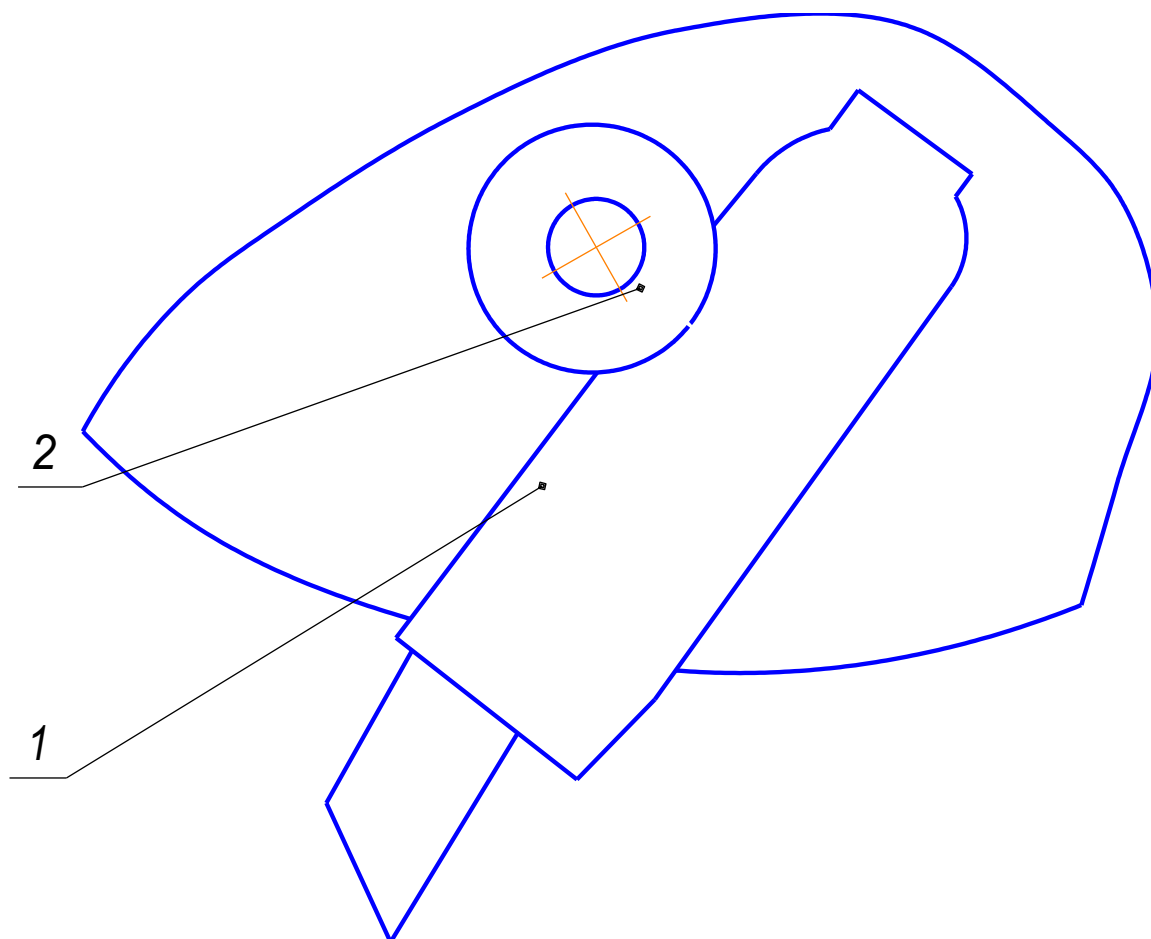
Схема крепления инструмента в револьверной головке
